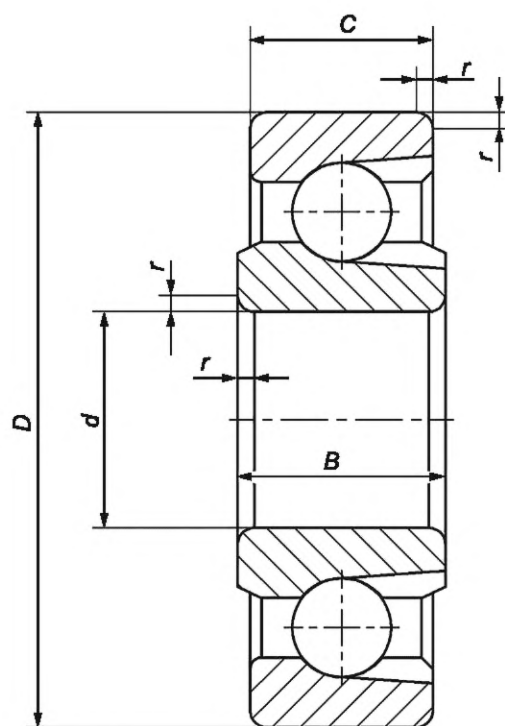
Конструктивное исполнение 90, шариковый радиальный однорядный подшипник
